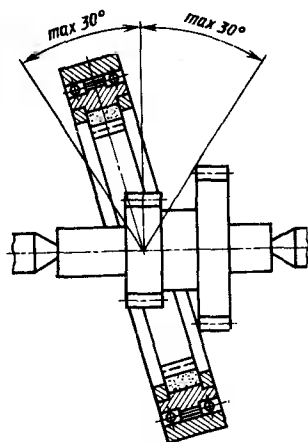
Схема хонингования зубчатого колеса хонем с внутренними зубьями
